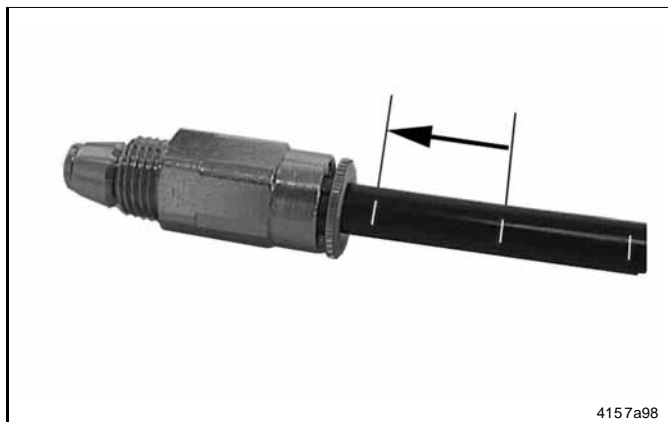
Rückschlagventil mit gerändelter Zange für Druckkunststoffrohr
